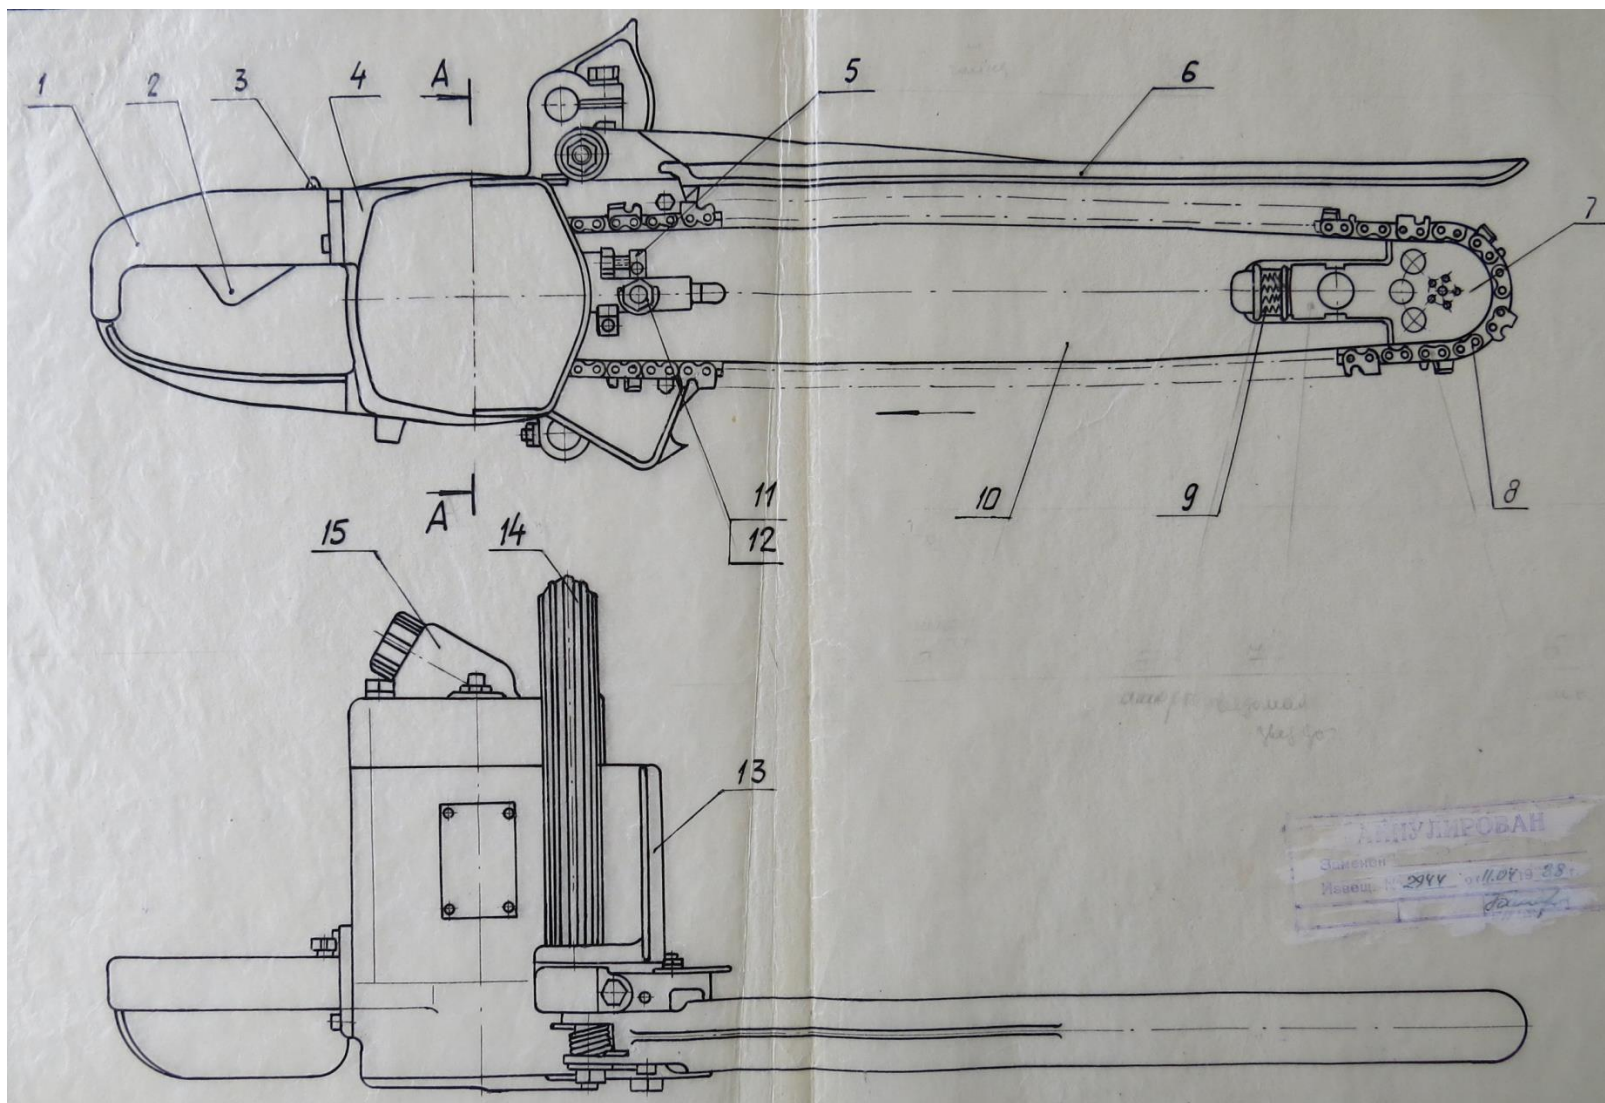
Схема пилки пневматичної ПШЛ2Б:
